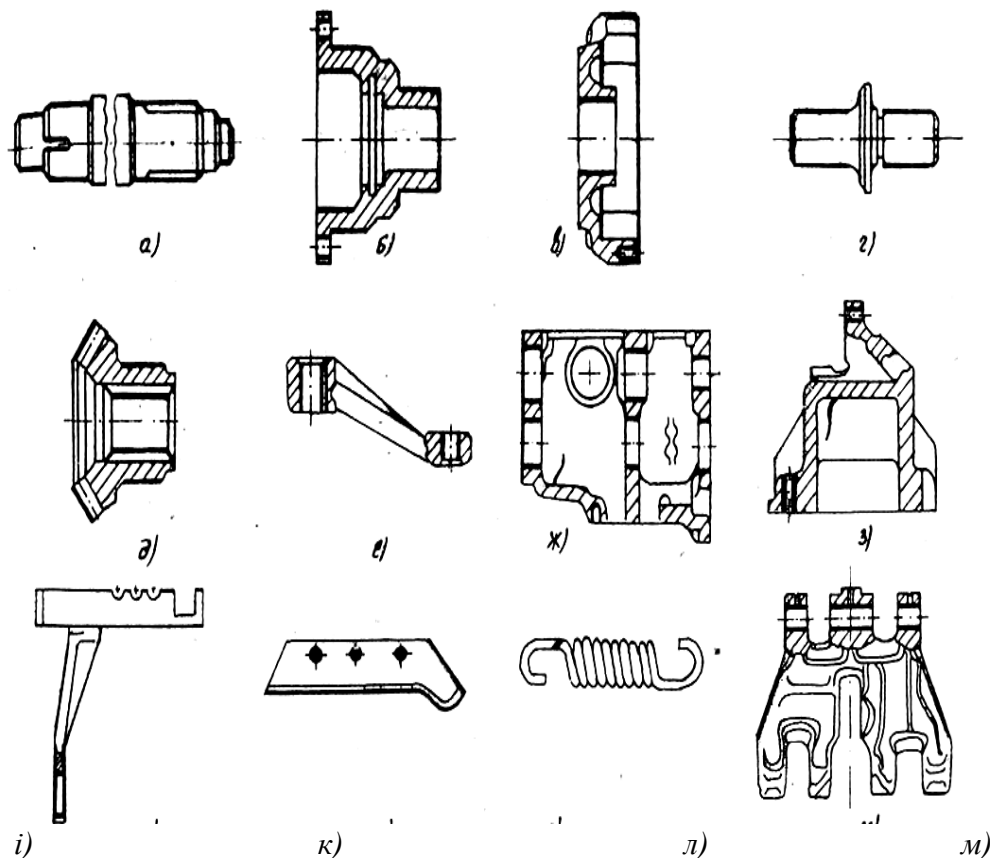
Ескізи деталей: а) – клас 01 – стрижні круглі; б) – клас 02 – циліндри порожнисті; в) – клас 03 - диски; г) – клас 04 – деталі дрібні; д) – клас 05 – колеса зубчасті; е) – клас 06 - важелі; ж) – клас 07 - деталі корпусні; з) – клас 08 - деталі просторові тонкостінні; и) – клас 09 - деталі площинні; к) – клас 10 - деталі профільні; л) – клас 11 - пружини, ресори; м) – клас 12 – деталі спеціальні.
